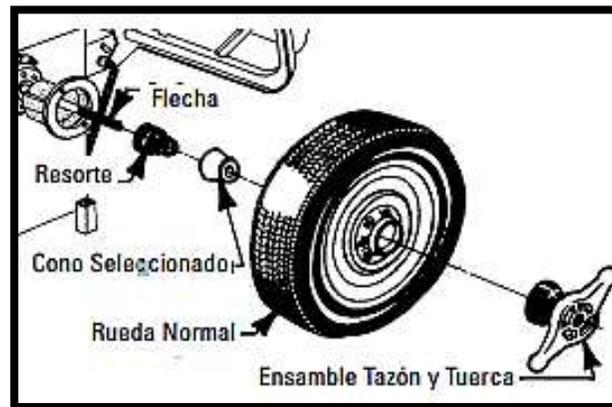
Montaje de neumático con cono posterior en máquina balanceadora
